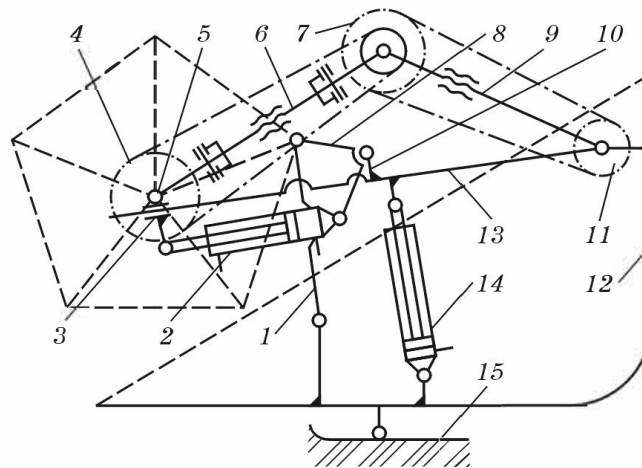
Схема зблокованого механізму регулювання положення мотовила:
